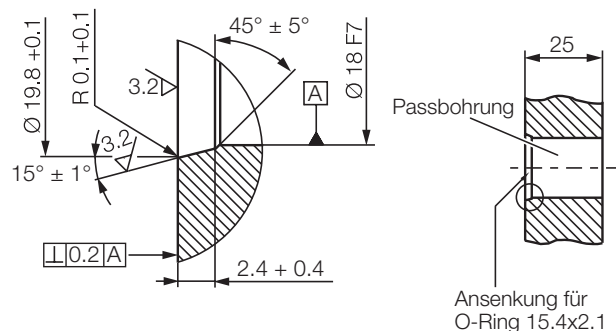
Passbohrung für die Montage des BTL mit O-Ring
